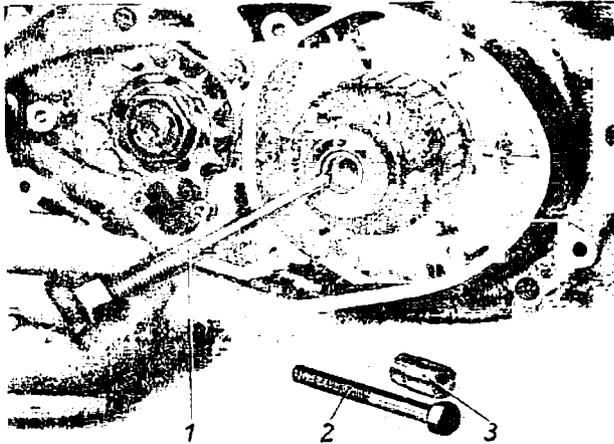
Abziehen des Lichtmaschinenankers mit Abdruckschraube Nr. 0100027 (1). 2 = Ankerbefestigungsschraube, 3 = Unterbrechnocken
